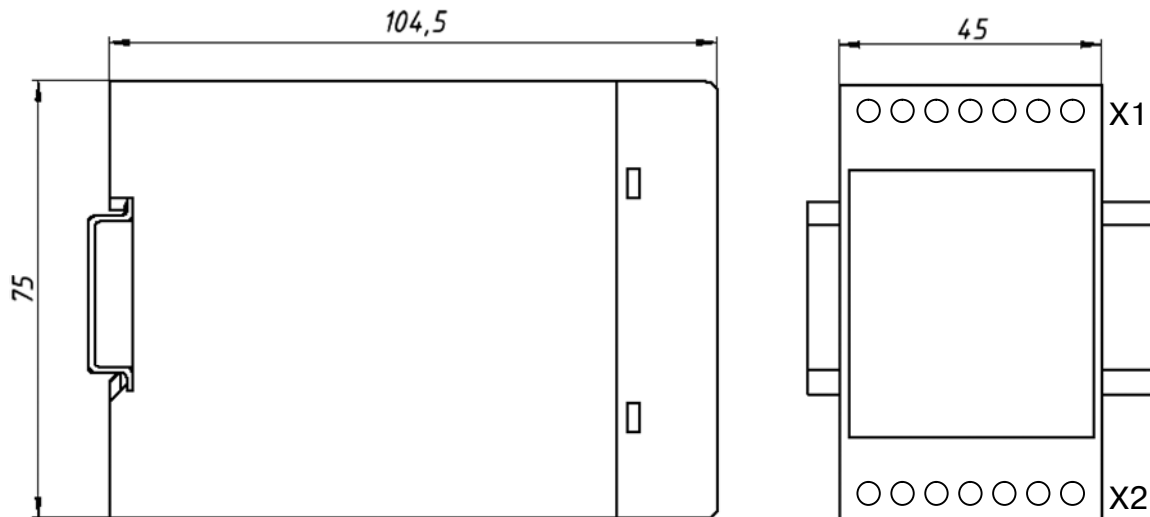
Габаритные и присоединительные размеры преобразователя
